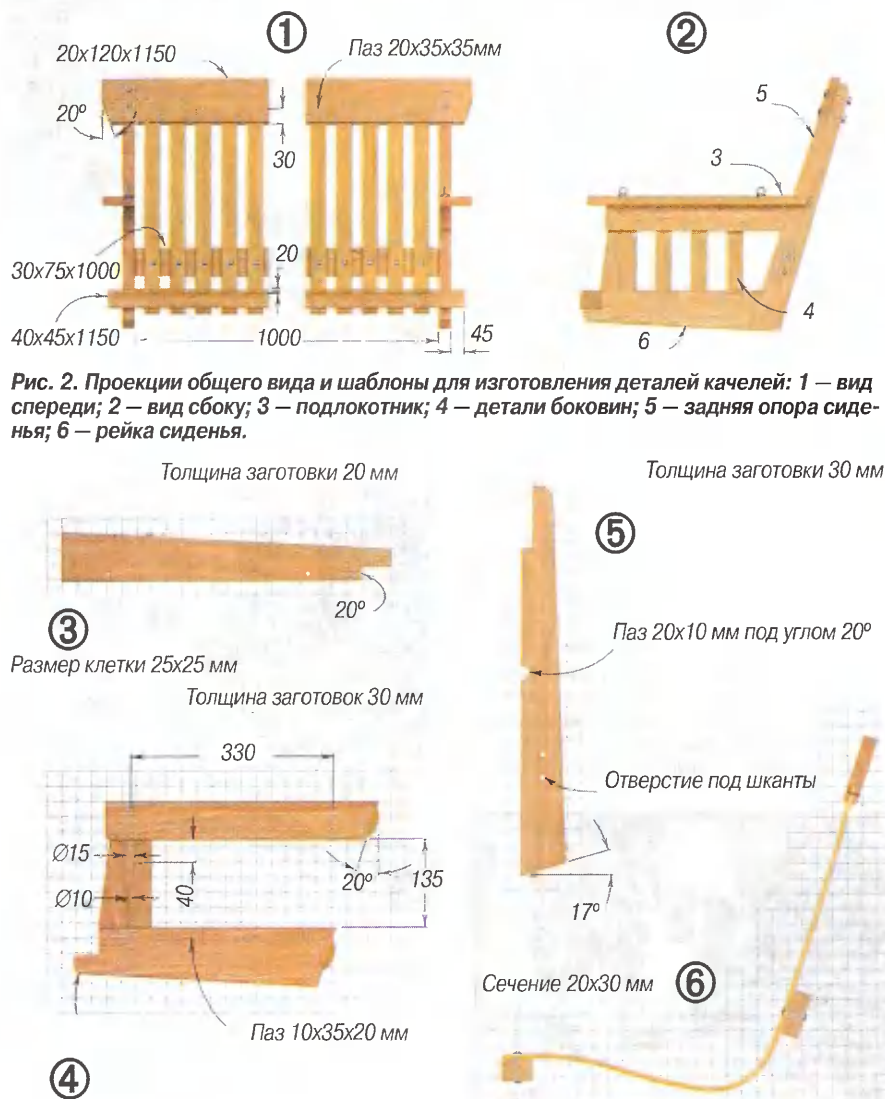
Проекция общего вида и шаблоны для изготовления деталей качелей: 1 — вид спереди; 2 — вид сбоку; 3 — подлокотник; 4 — детали боковин; 5 — задняя опора сиденья; 6 — рейка сиденья.
